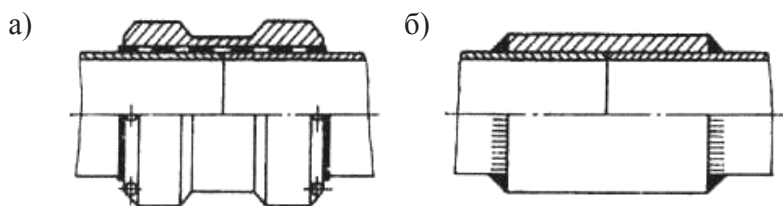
Схемы неразъемных соединений трубопроводов, выполненных с помощью пайки (а) и сварки (б)
